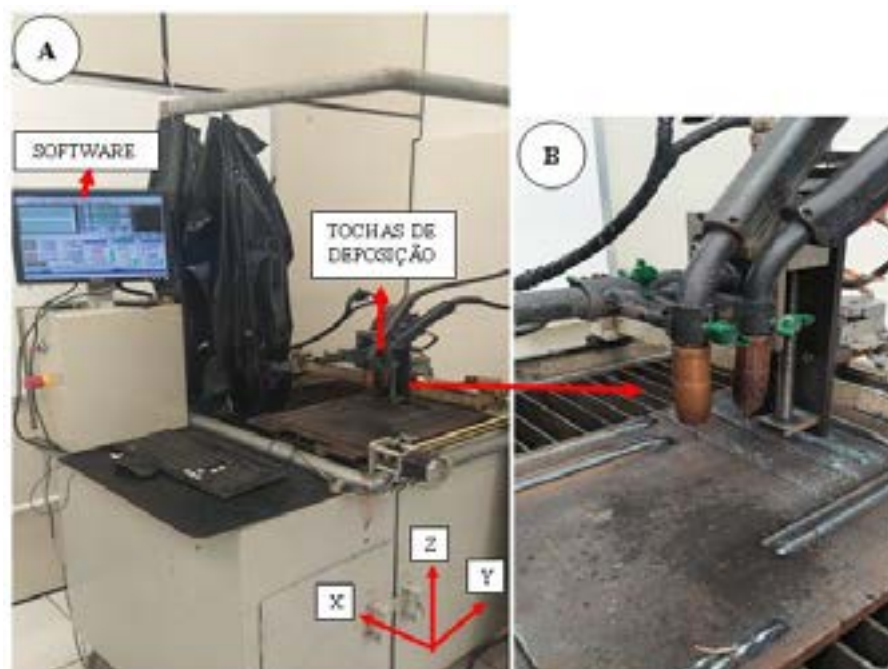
Equipamento para fabricação das amostras. Do autor, 2023.
